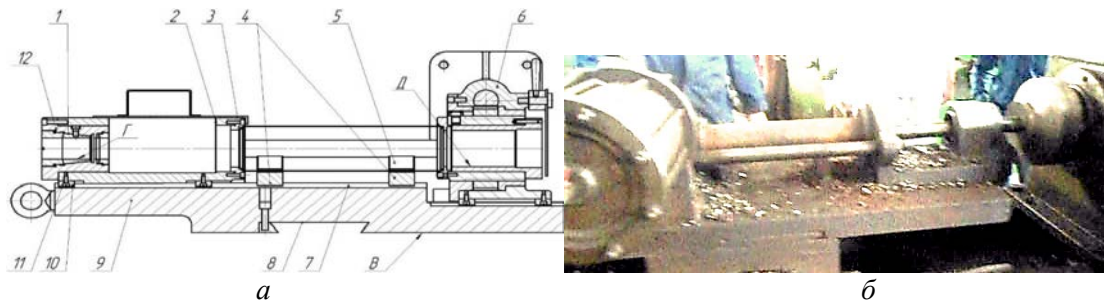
Установка для оброблення внутрішньої циліндричної поверхні підсилвача рульової колонки автомобіля марки «КРАЗ»: а – принципова конструктивна схема; б – фрагмент установки
